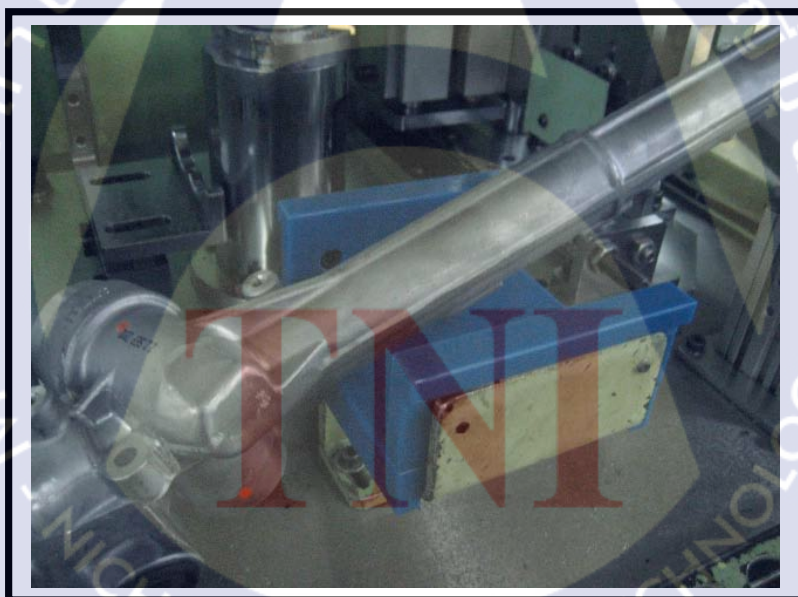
แสดงแบบ Jig support needle bearing ฝั่งซ้าย และ ฝั่งขวา
